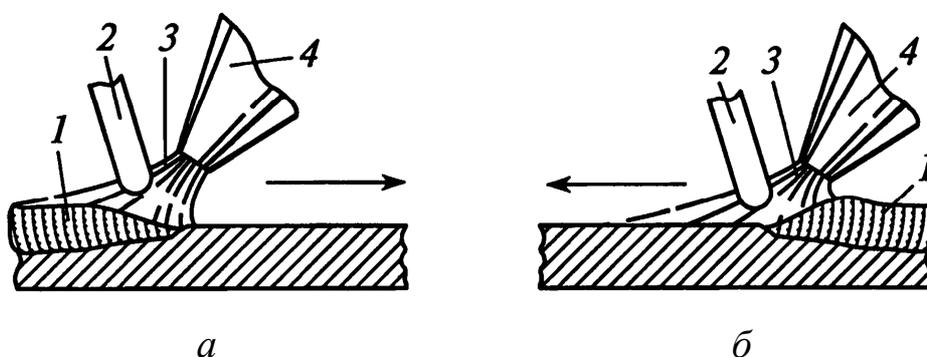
Основные способы газовой сварки: *а* – правый способ сварки; *б* – левый способ сварки; 1 – формирующий шов; 2 – присадочный пруток; 3 – пламя горелки; 4 – горелка
